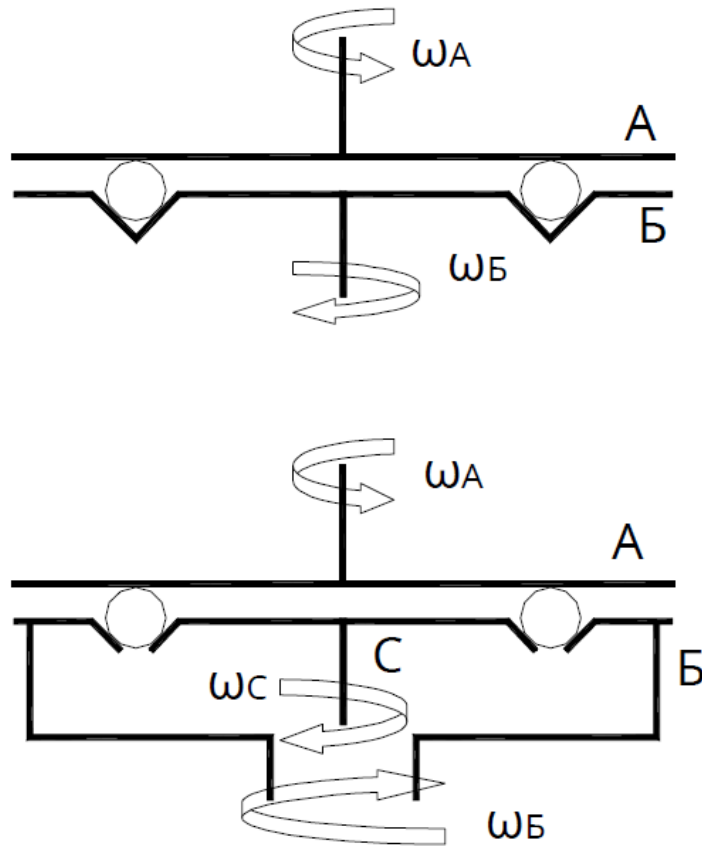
Схема шліфування абразивним інструментом з верхнім розташуванням та диску з V-подібною канавкою.
